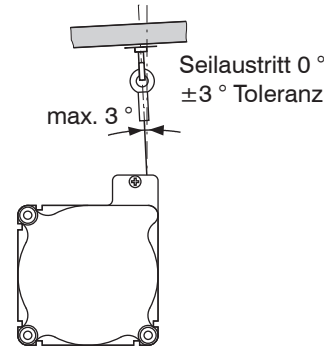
Befestigung und maximaler Schrägzug des Messseils
